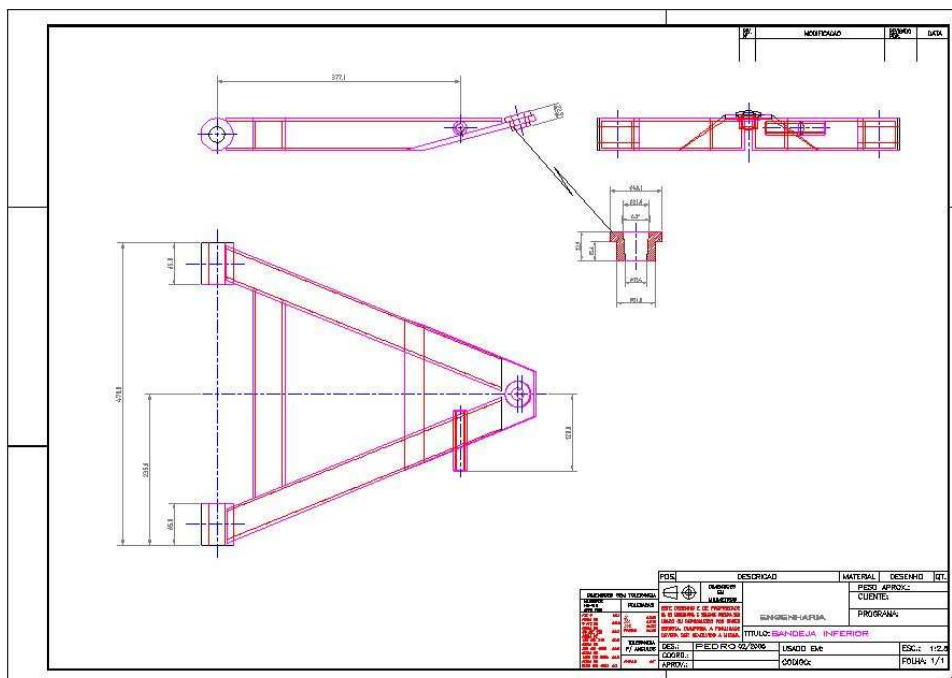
Desenho de fabricação de uma bandeja inferior de suspensão. Como a peça deste desenho é soldada e não forjada, outras cotas devem ser mostradas em outros desenhos relativos a cada item deste componente.
